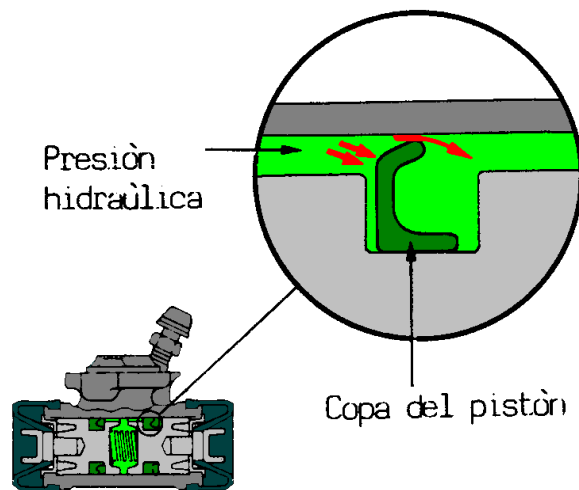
Cilindro de rueda de tambor instalado incorrectamente.
